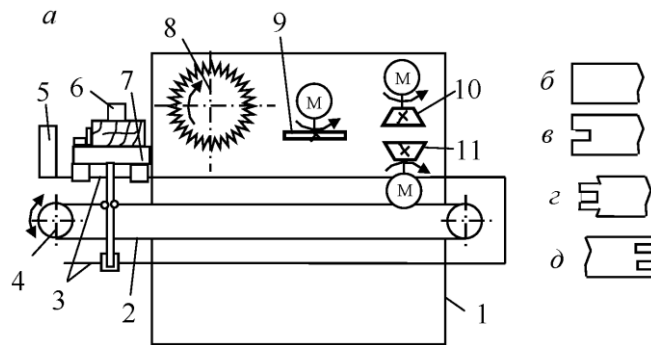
Однобічний рамний шипорізний верстат ШО15Г-5: *а* - технологічна схема; *б* - заготівка після обробки пилкою; *в* - заготівка після обробки провувшечним диском; *г* - готові кінці деталі
